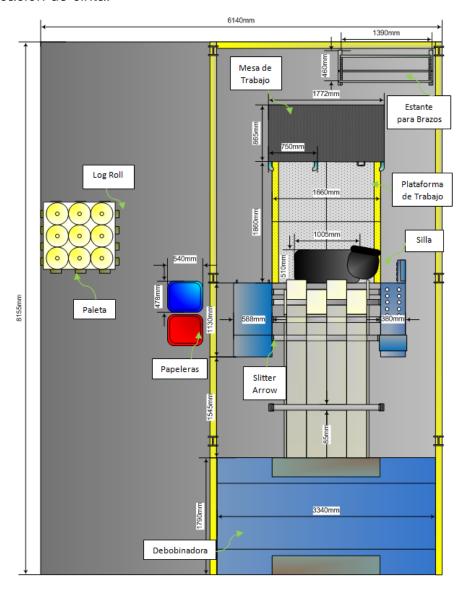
Vista de planta dimensionada del área de fabricación de cinta.
